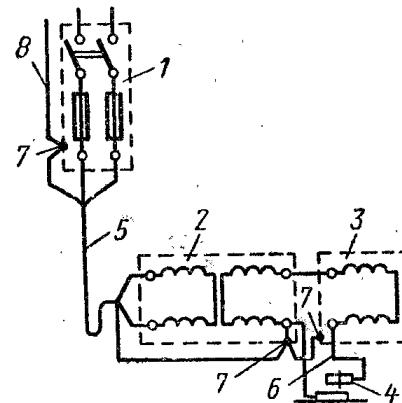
Заземление (зануление) сварочного трансформатора.
